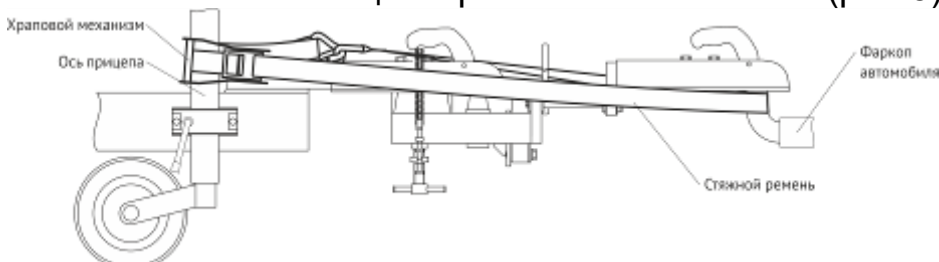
Внешний вид нагрузателя со стяжным ремнем
